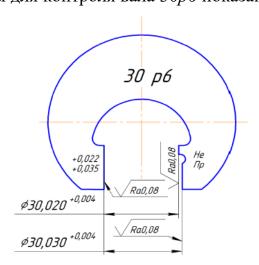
Эскиз калибра-скобы для контроля вала 30p6 41
